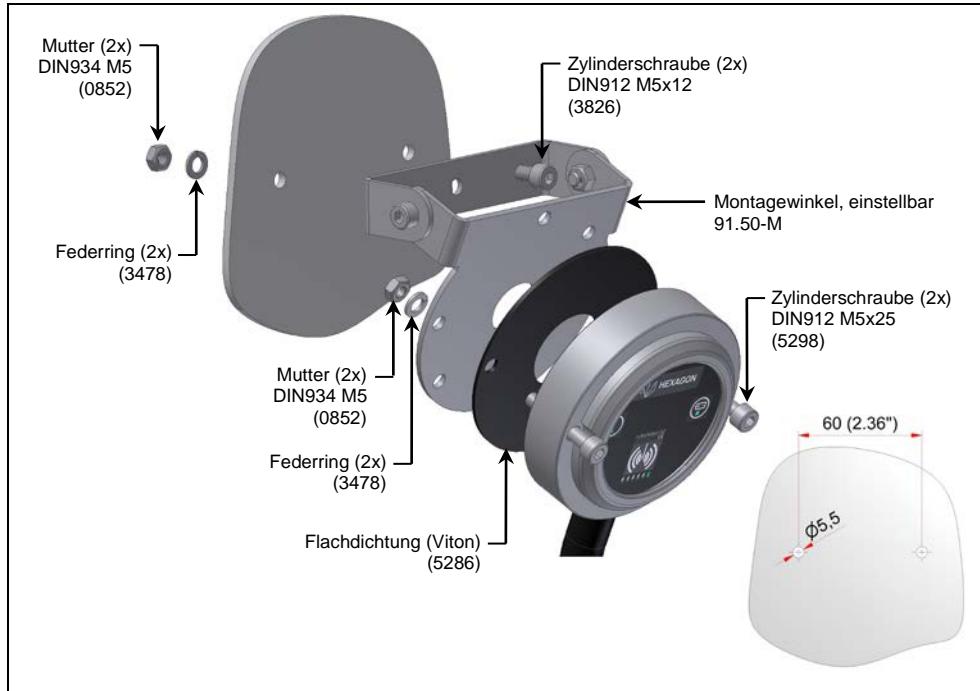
Montage RWR95.50-R mit Montagewinkel
